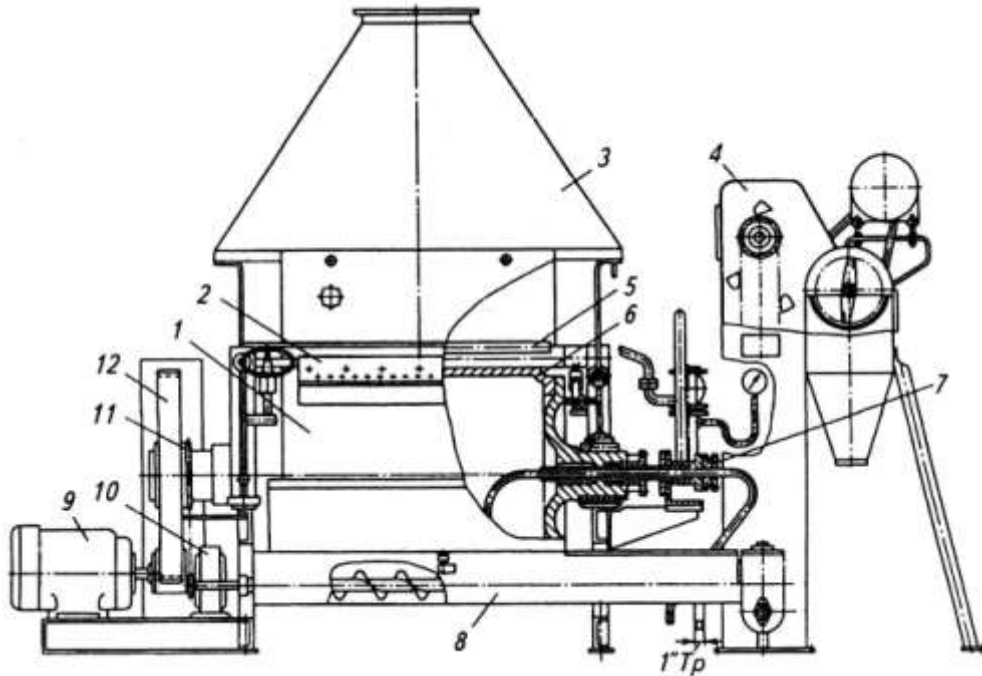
Сушильно-подрібнювальний агрегат СДА-250:
